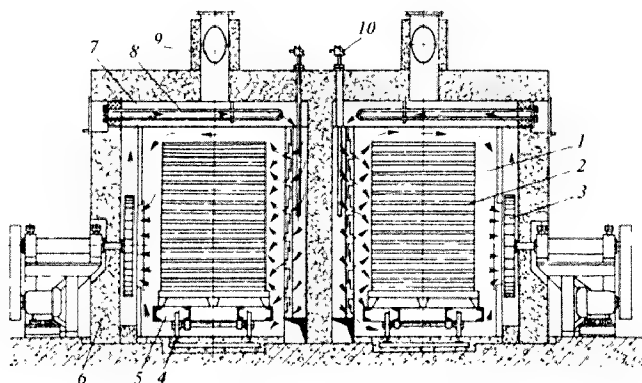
Бакелизатор (вулканизатор) двухкамерный:
